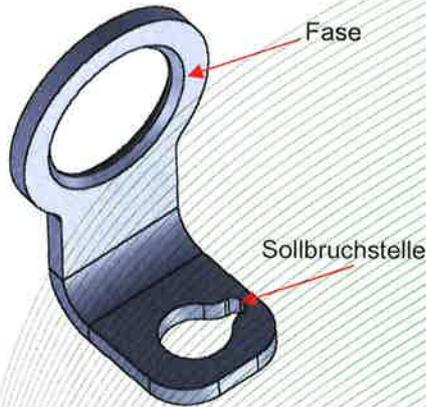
Anschlagpunkt, Typ: TS-Lasche (TS-011) (mit Sollbruchstelle, mit Fasen (2 x 45°))
